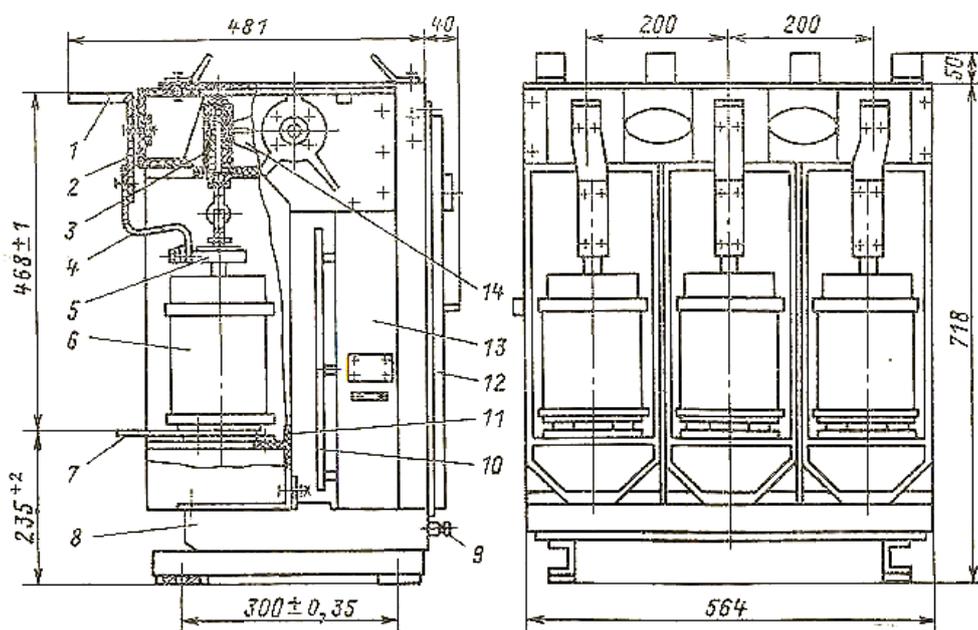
Вакуумный выключатель ВВТЭ-10-10/630 У2
